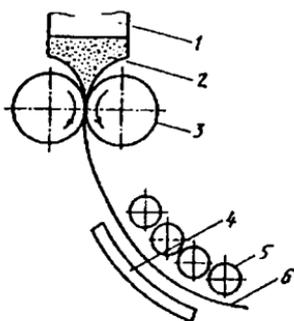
Схема прокатки порошка: 1 — бункер; 2 — порошок; 3 — валки; 4 — направляющая; 5 — ролики; 6 — прокатанная лента
